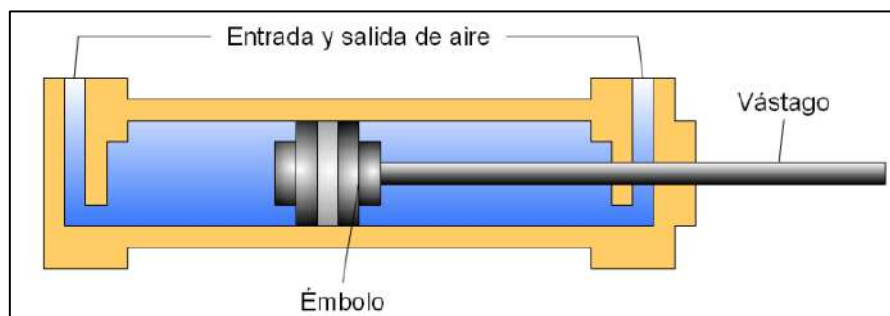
Partes de un cilindro neumático de doble efecto [26].
